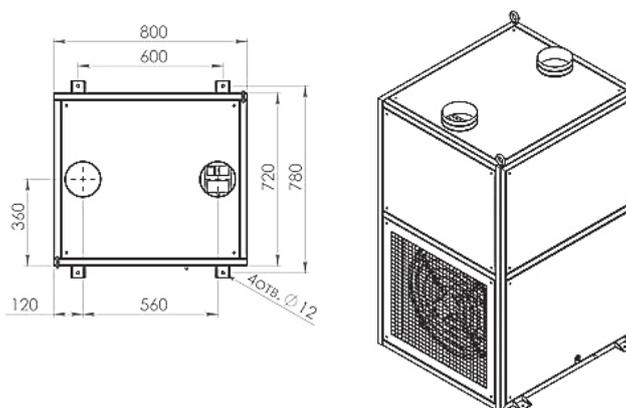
Габаритный чертеж кондиционера «Аю-Даг 04»
